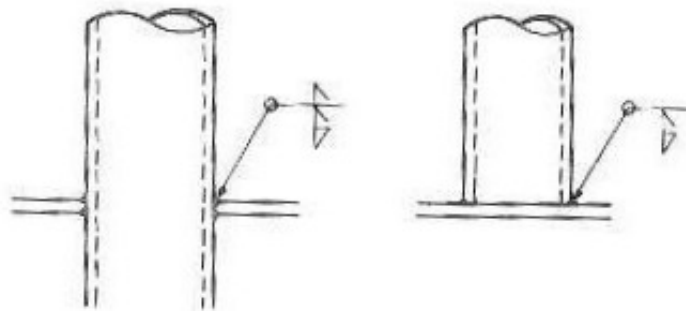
単一鋼管部材の端部の溶接方法 (d = 1 / 25)
